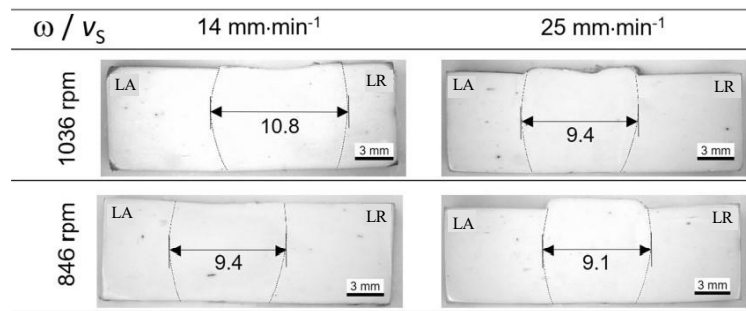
Secção transversal das amostras soldadas, [23].
